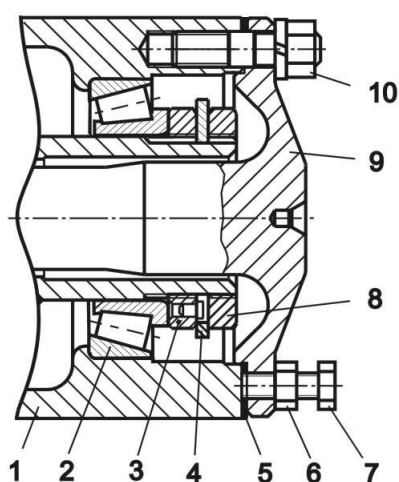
Крепление ступицы заднего колеса (ПАЗ-32053-07)
